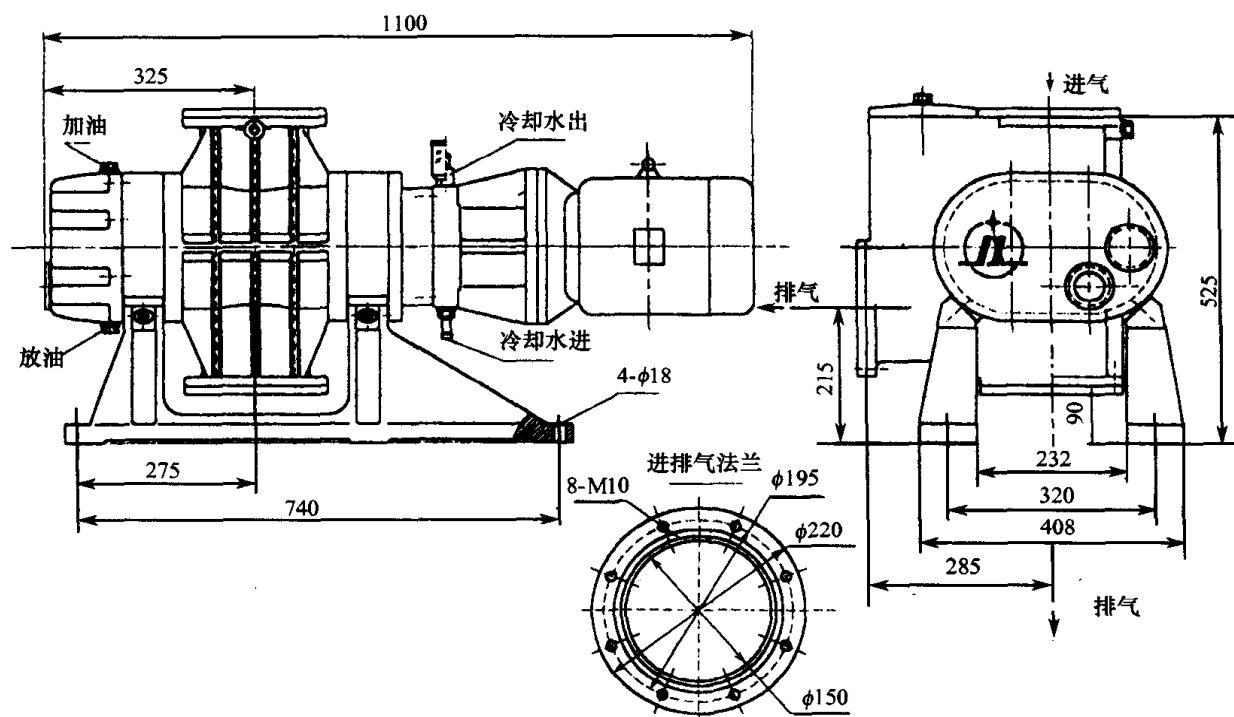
ZJP-300 型罗茨泵外形及安装尺寸
